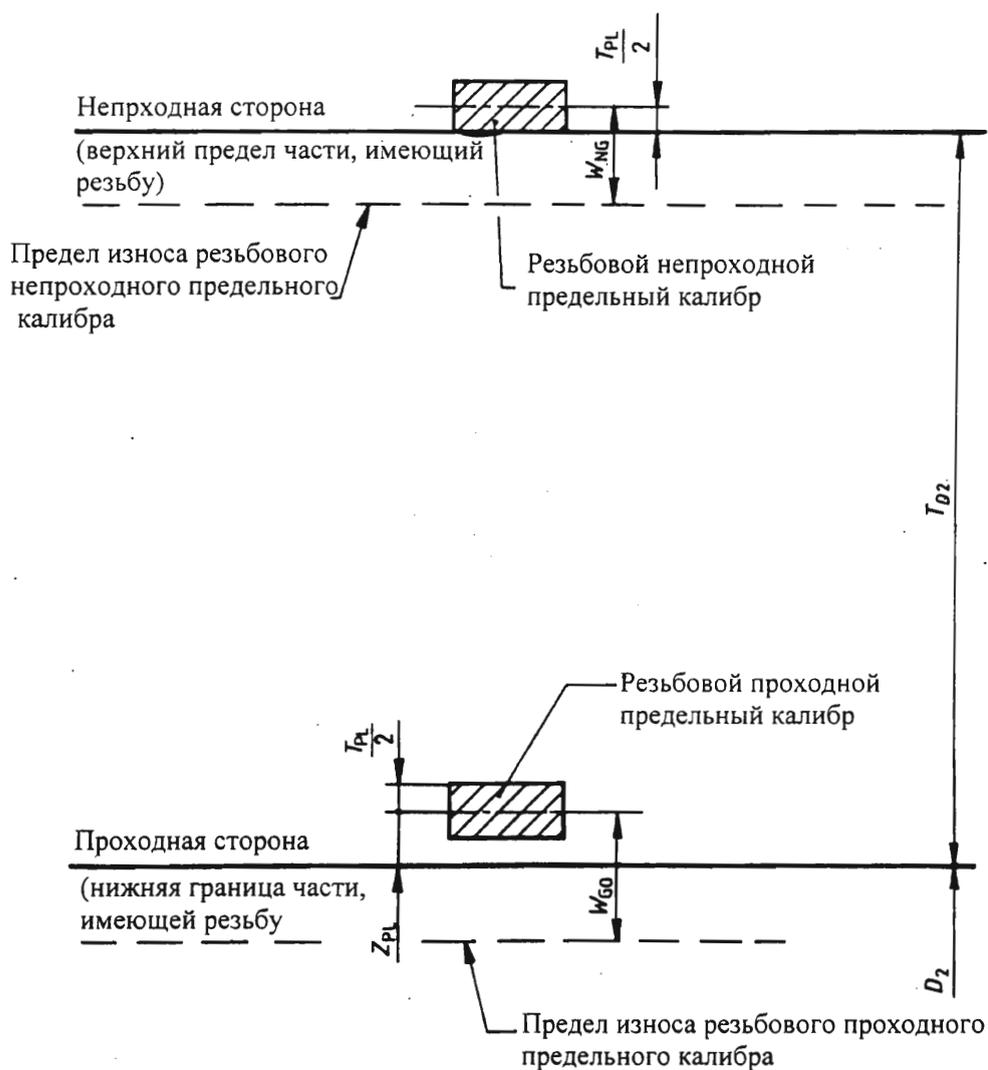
Относительное положение полей допуска на средний диаметр резьбы
